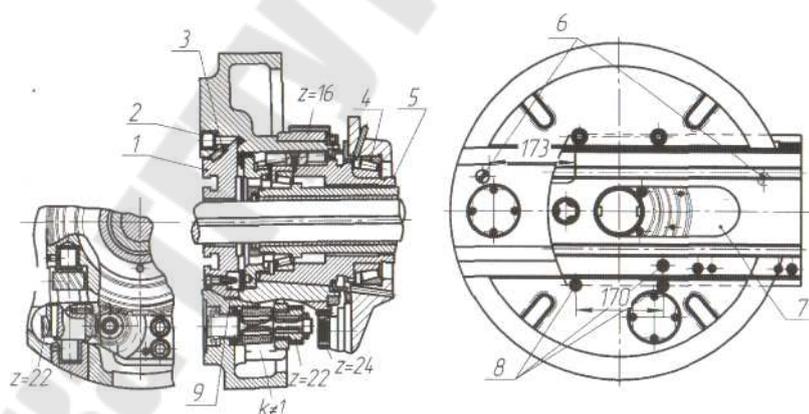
Планшайба с радиальным суппортом станка модели 262Г
